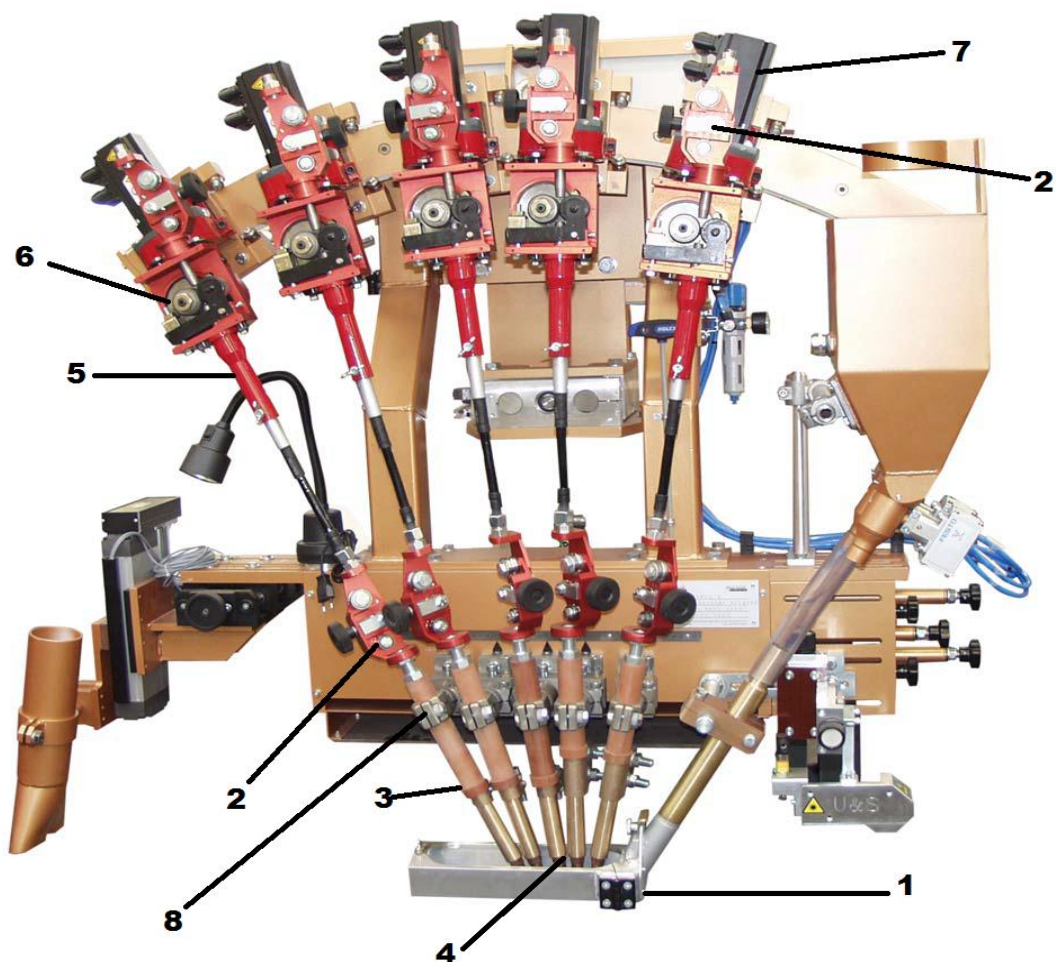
Устройство сварочной головки: 1-Механизм подачи флюса; 2- Правильный механизм; 3-Токопроводящее устройство; 4-Токопроводящий мундштук; 5-Коменсаторная гильза; 6-Прижимной ролик; 7-Мотор-редуктор; 8-Поворотно-зажимное устройство
